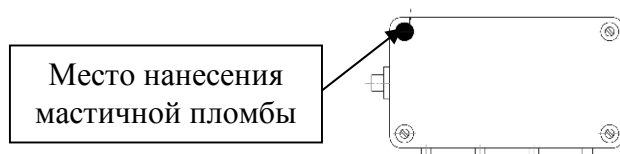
Схема пломбировки корпуса динамического преобразователя
